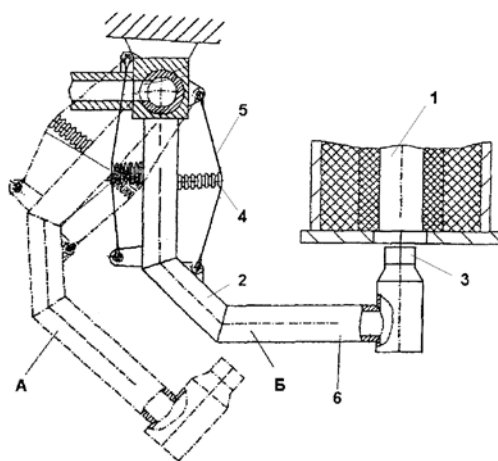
Устройство для закрывания выпускного отверстия конвертера
